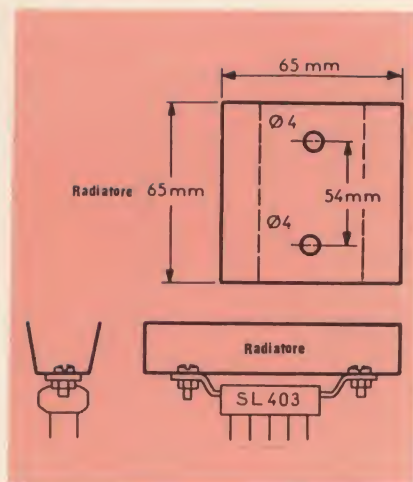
Dimensioni d'ingombro del dissipatore da applicare al circuito integrato del modulatore.
